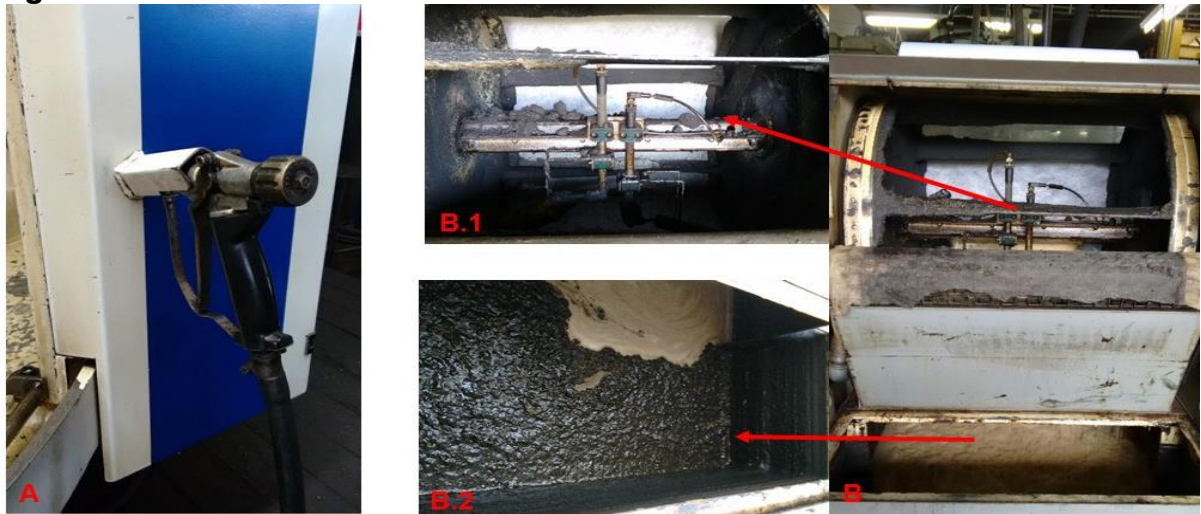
Máquina utilizada para coleta de fluido de corte, centro de usinagem HELLER MCI25.
